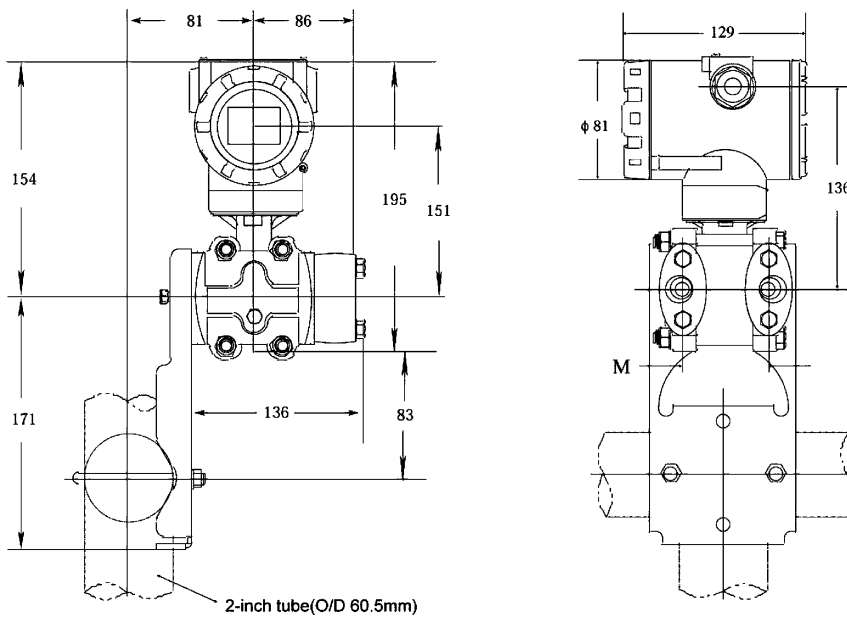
Типовые схемы установки. Крепление на вертикальной трубе.
